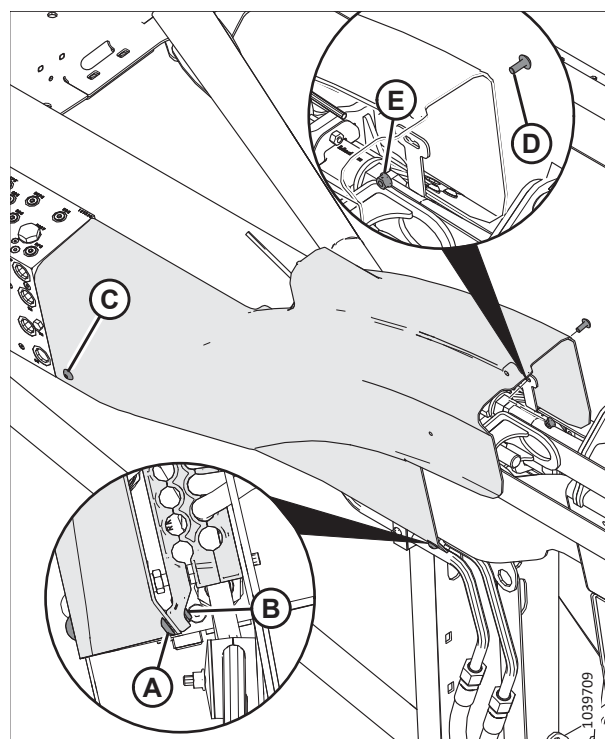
Levý kryt spojovacího ústrojí – zadní část adaptéru
